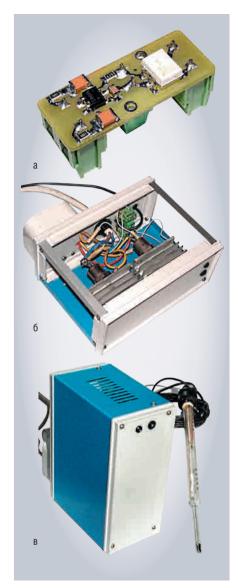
Внешний вид устройства и его элементов: а) плата управления (вид со стороны дорожек); б) устройство в корпусе со снятой крышкой; в) общий вид устройства в сборе
